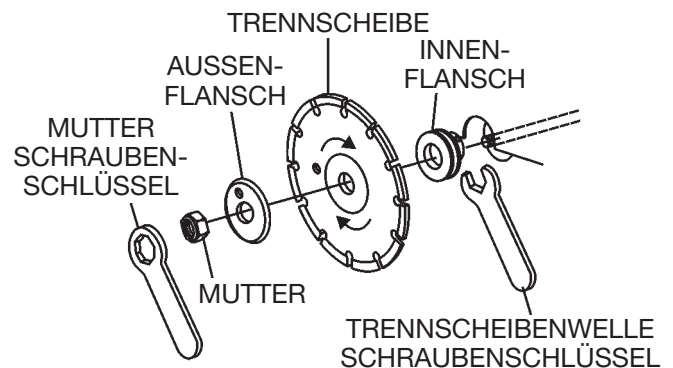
Schraubenschlüssel zur Trennscheibenbefestigung
